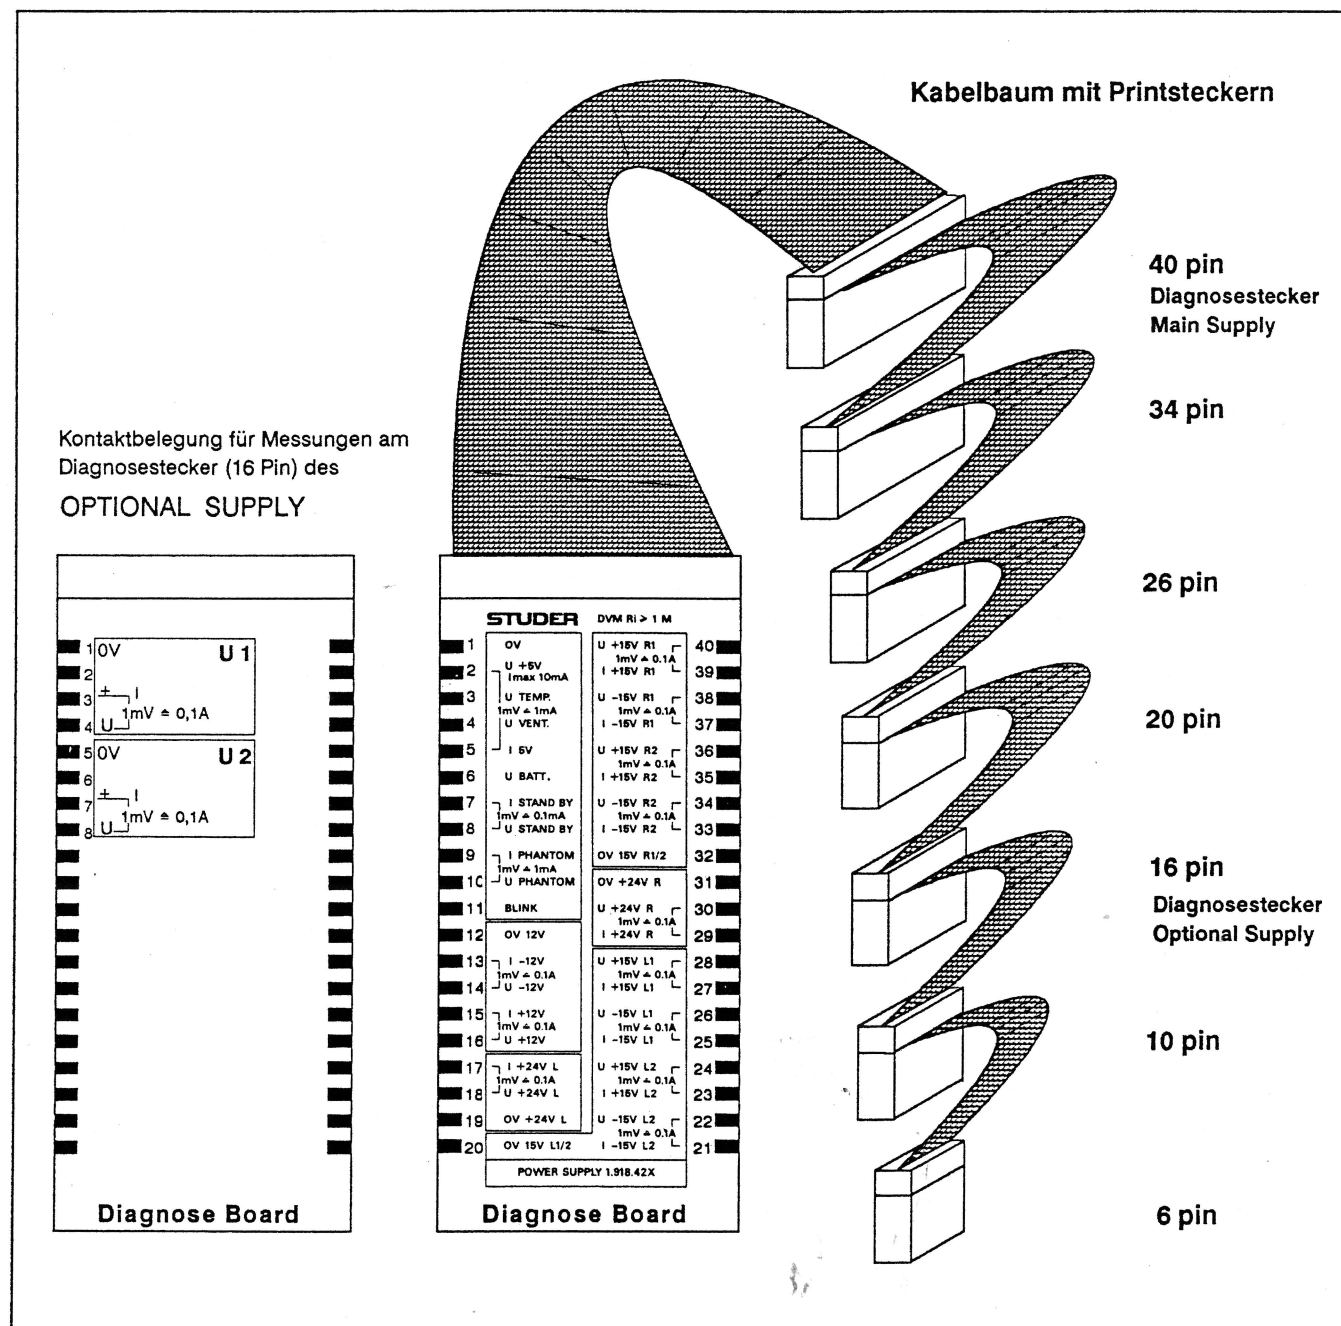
Diagnose-Board 1.918.080 mit universell einsetzbarem Kabelbaum. Links sind die Messwerte für den Diagnosestecker der Optionen 1 und 2 aufgeführt.
